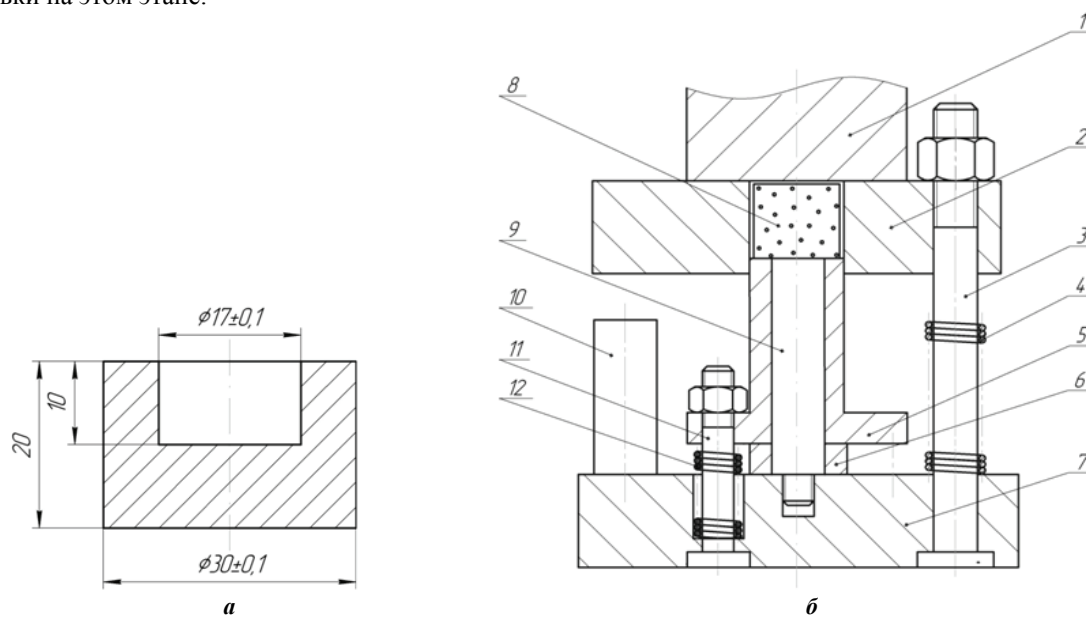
Чертеж детали «заглушка» – а и схема штампа – б
